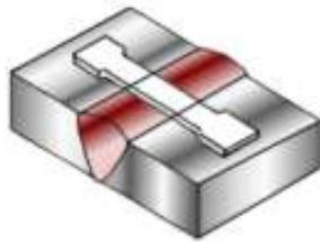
Prélèvement de l'éprouvette dans la soudure.
